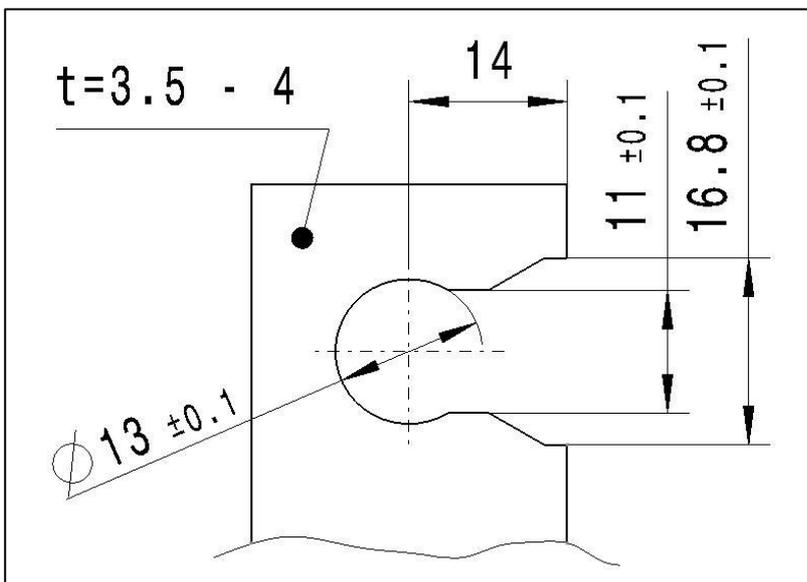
Dimensiones del soporte para el cable del freno de mano
